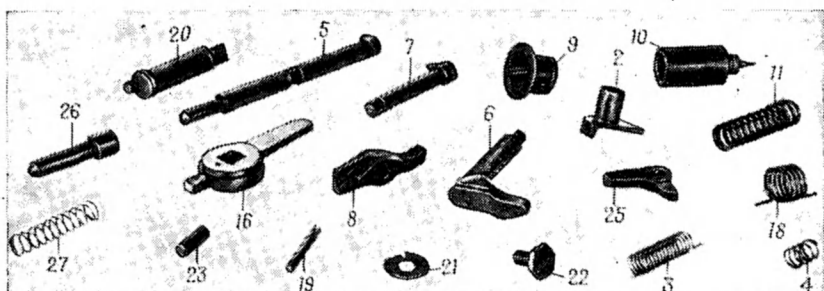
Детали ударного механизма, повторного взвода, ударника и предохранителя:
